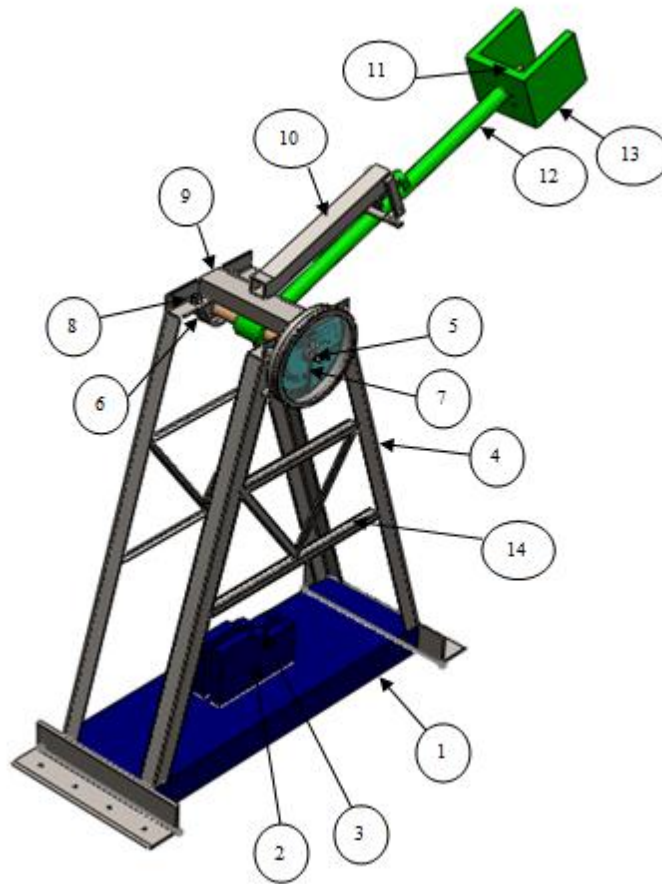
Partes de la máquina Charpy. (Fuente: El autor)
